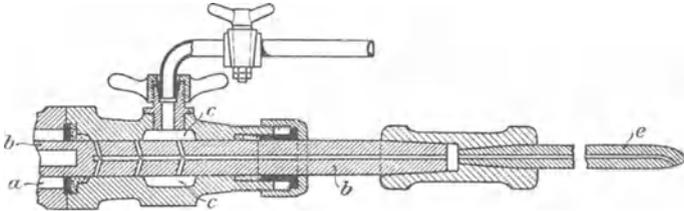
Wasserspüleinrichtung an Stoßbohrmaschinen.
